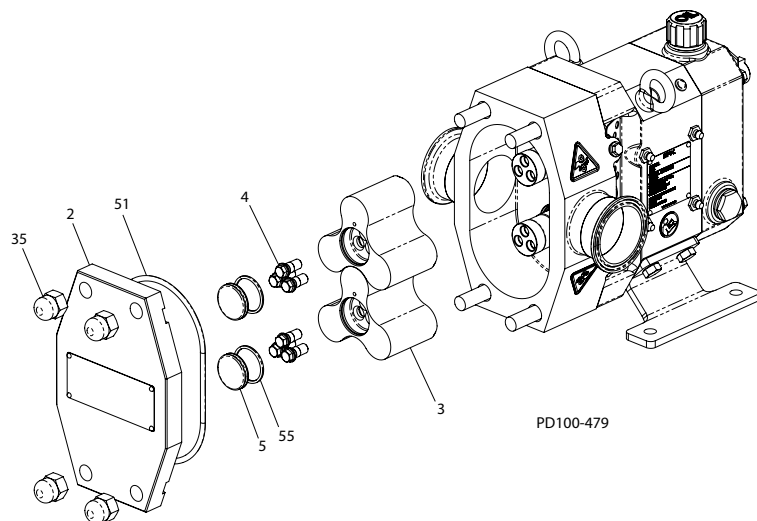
Pumpenabdeckung und Rotor entfernen
